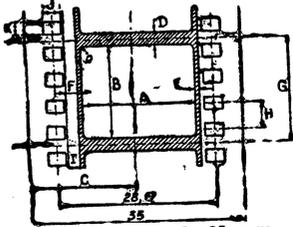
Le film de 35 mm. A = 22,05 + ou - 0,05; B = 16,03 + ou - 0,05; C = 18,90 + ou - 0,05; D = 2,97; E = 0,25 env.; F = 3,07 env.; G = 19; H = 4,75; R = 0,8 env.; I = 2,75; J = 2,75; K = 1,98.
